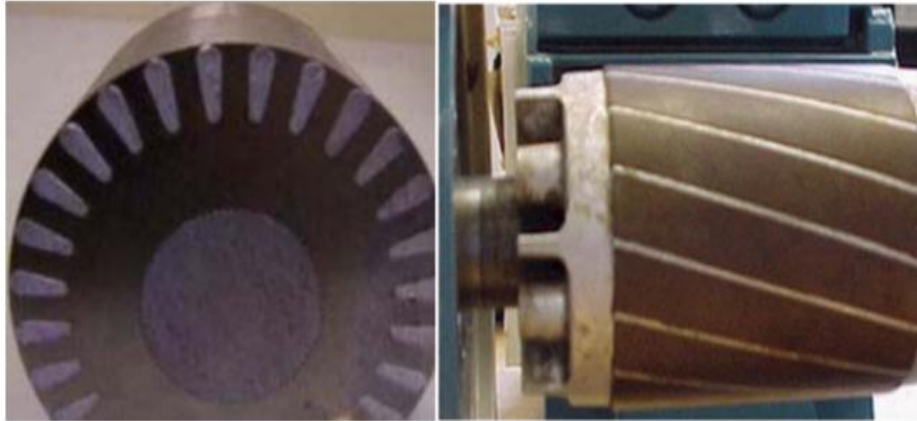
Photo du rotor d'une machine asynchrone.[26]
